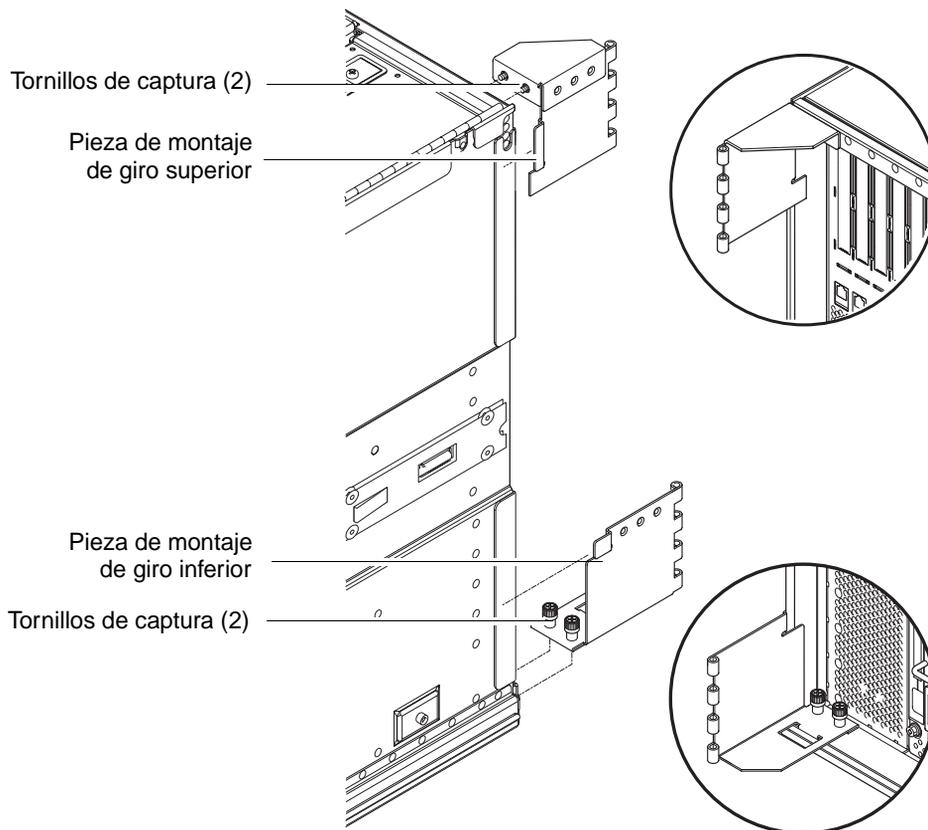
Instalación de las piezas de montaje de giro inferior y superior
